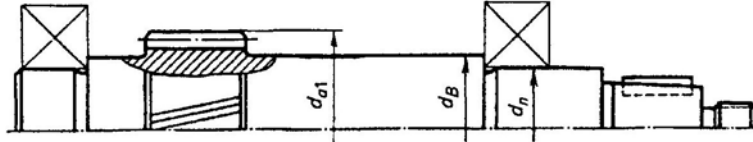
Вал-шестерня циліндричної косозубої передачі
